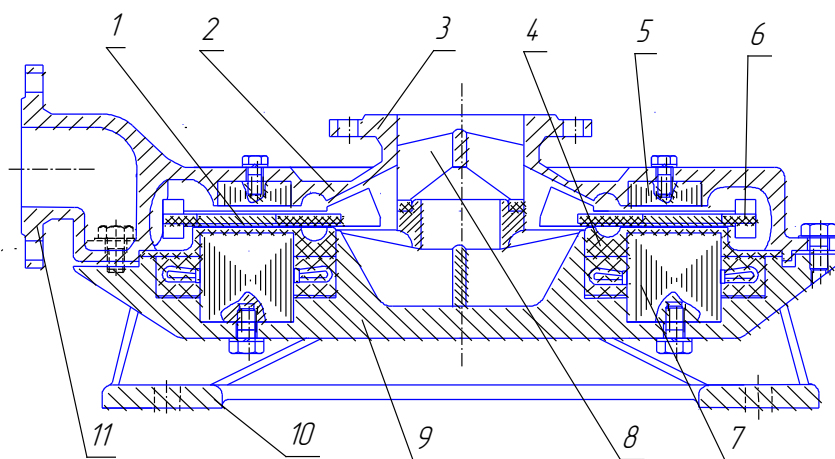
Центробежно-вихревой насос с рабочим колесом – «свободным» кольцевым ротором: 1 – рабочее колесо с кольцевым ротором; 2 – крышка насоса; 3 – фланец по подающей магистрали; 4 – пластиковый изолирующий колпак; 5 – дополнительный магнитопровод; 6 – лопасти рабочего колеса; 7 – индуктор силового поля; 8 – входной патрубок; 9 – корпус; 10 – крепление корпуса; 11 – фланец выходной горловины
